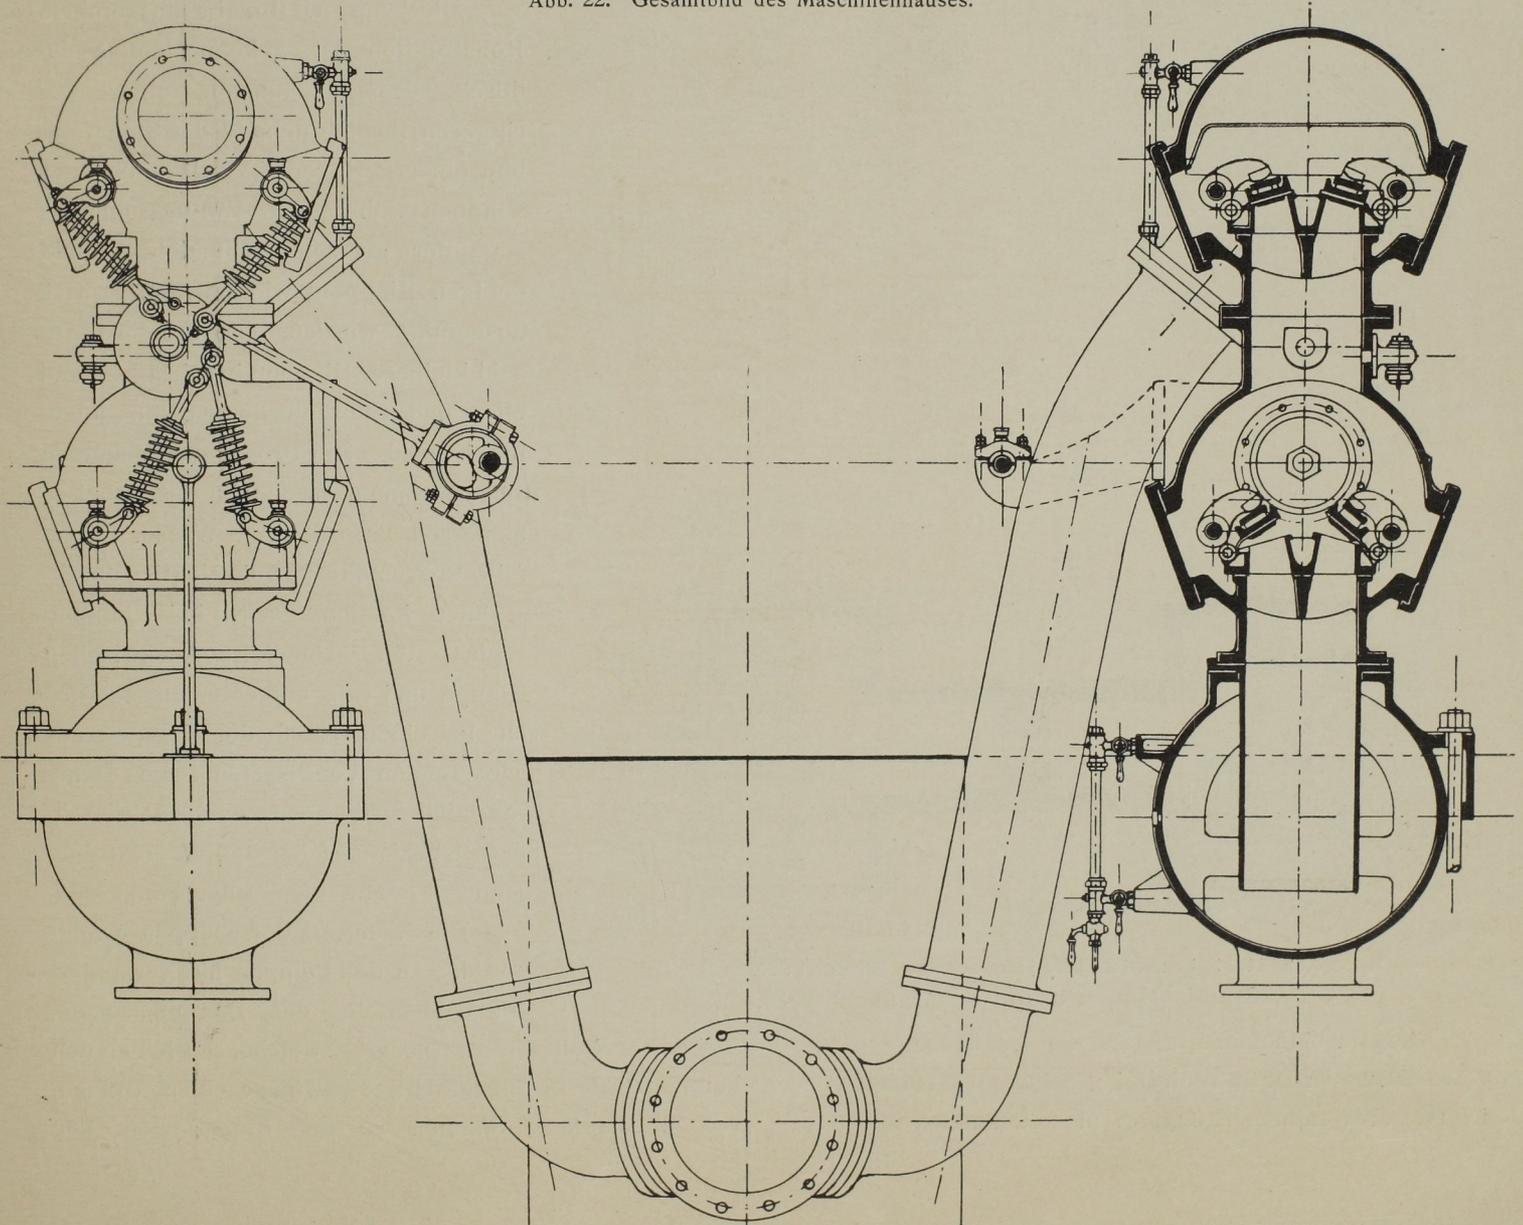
Seitenansicht und Querschnitt der Druckpumpen. Massst. 1:20.
